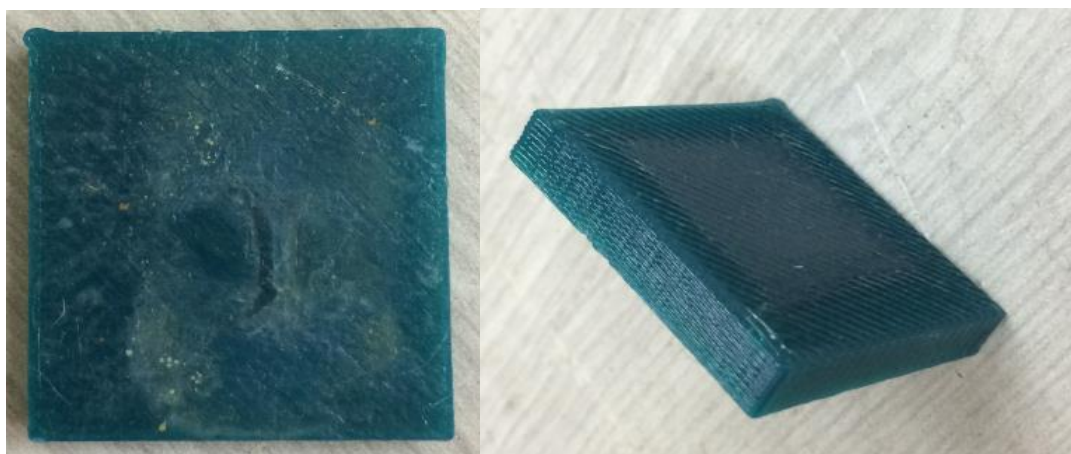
ГОТОВЫЙ испытываемый образец, изготовленный на 3D принтере
